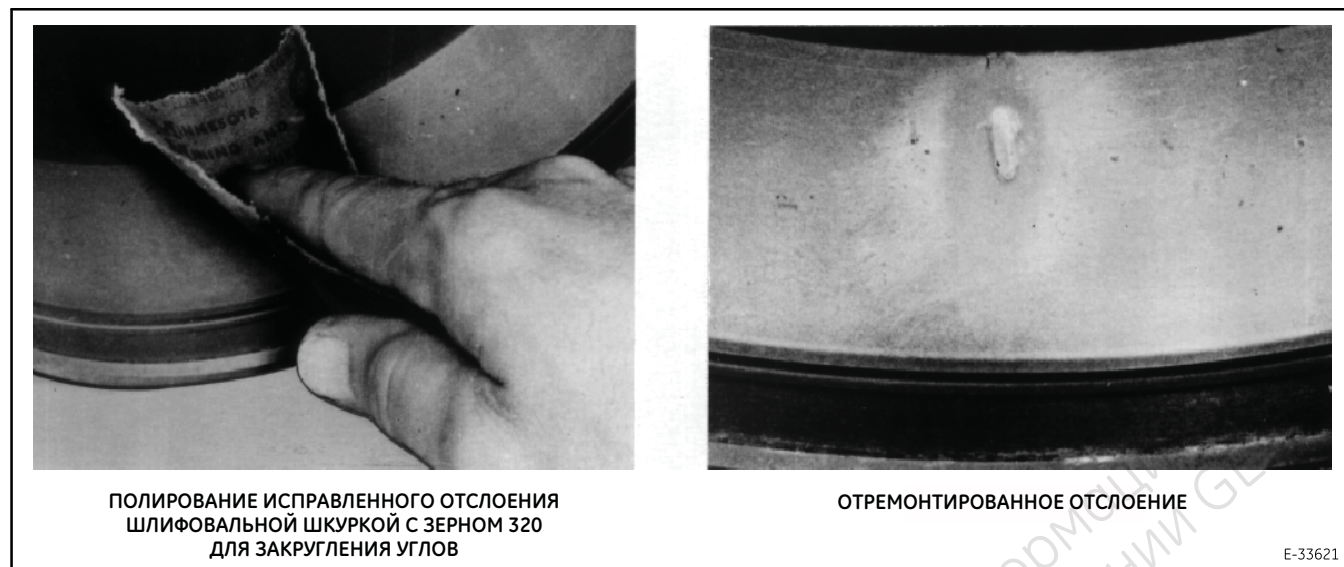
Метод исправления мелкого отслаивания металла на роликовой дорожке наружного кольца подшипника.
